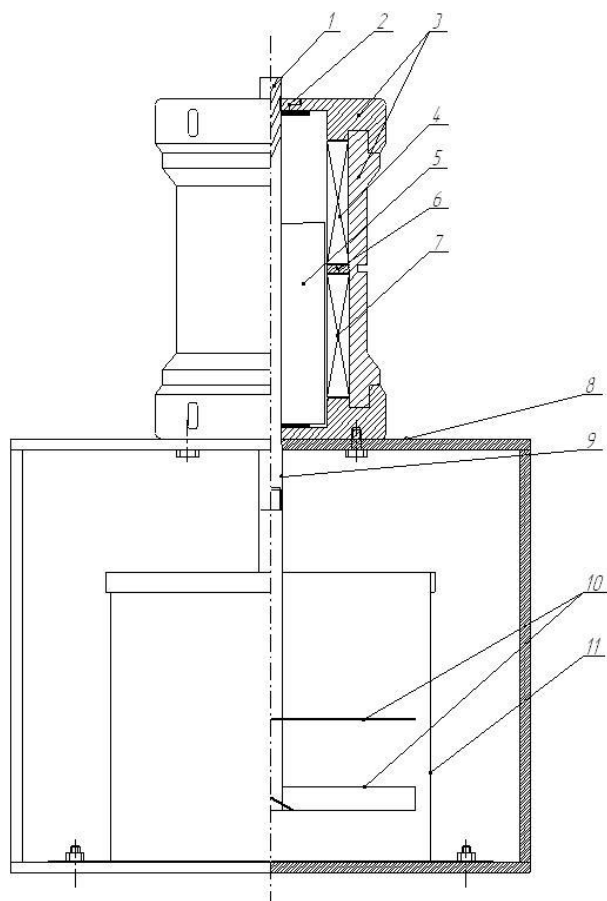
Маслообразовательный агрегат с двухобмоточным ЛЭМД
